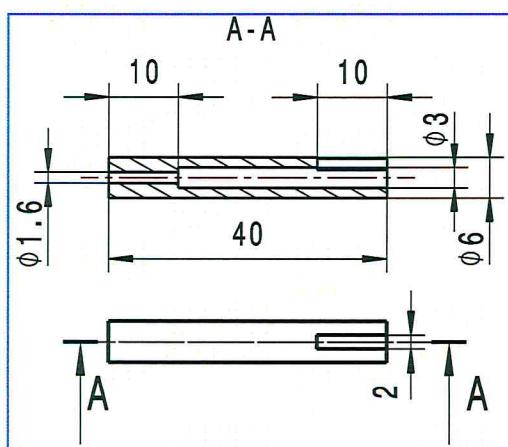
Schéma technického řešení adaptéra pro upevnění elektrody
